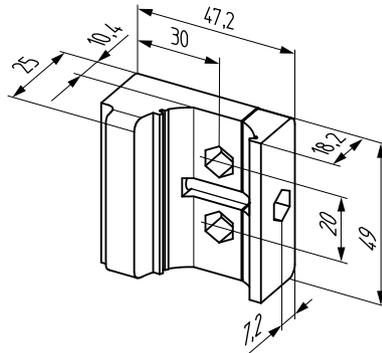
Croquis de dimensiones del soporte QuickFix (2066048)
